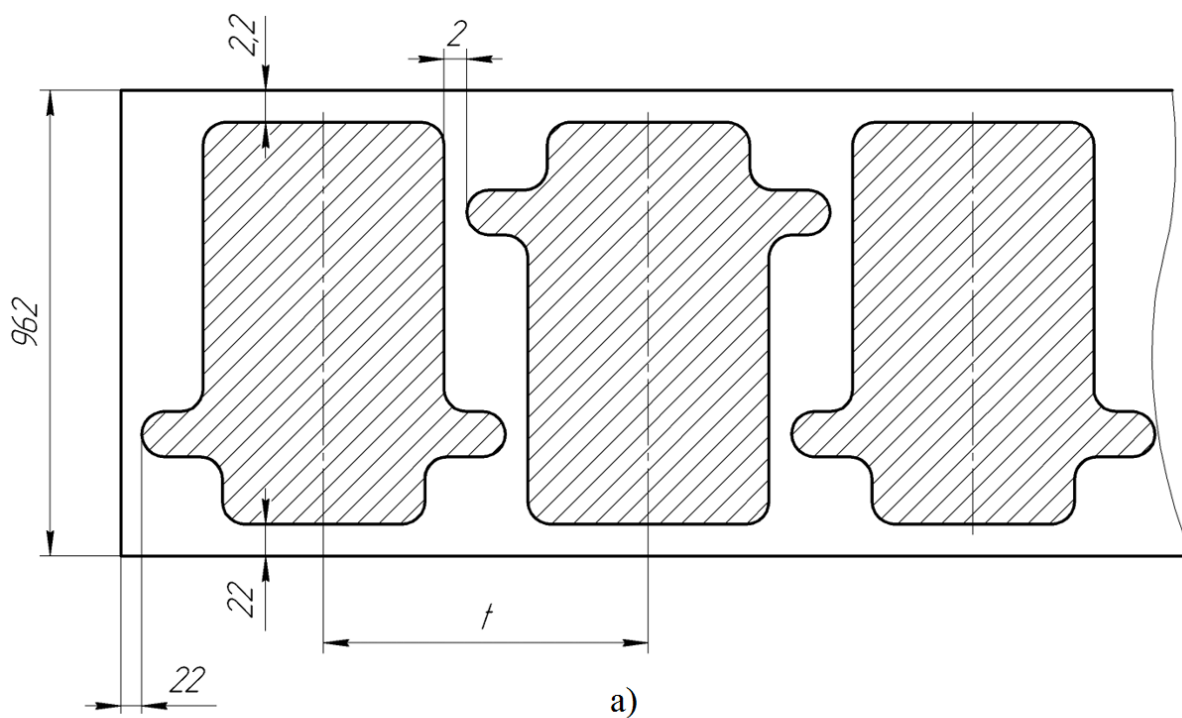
Варіанти схем розташування заготовок на смузі:
